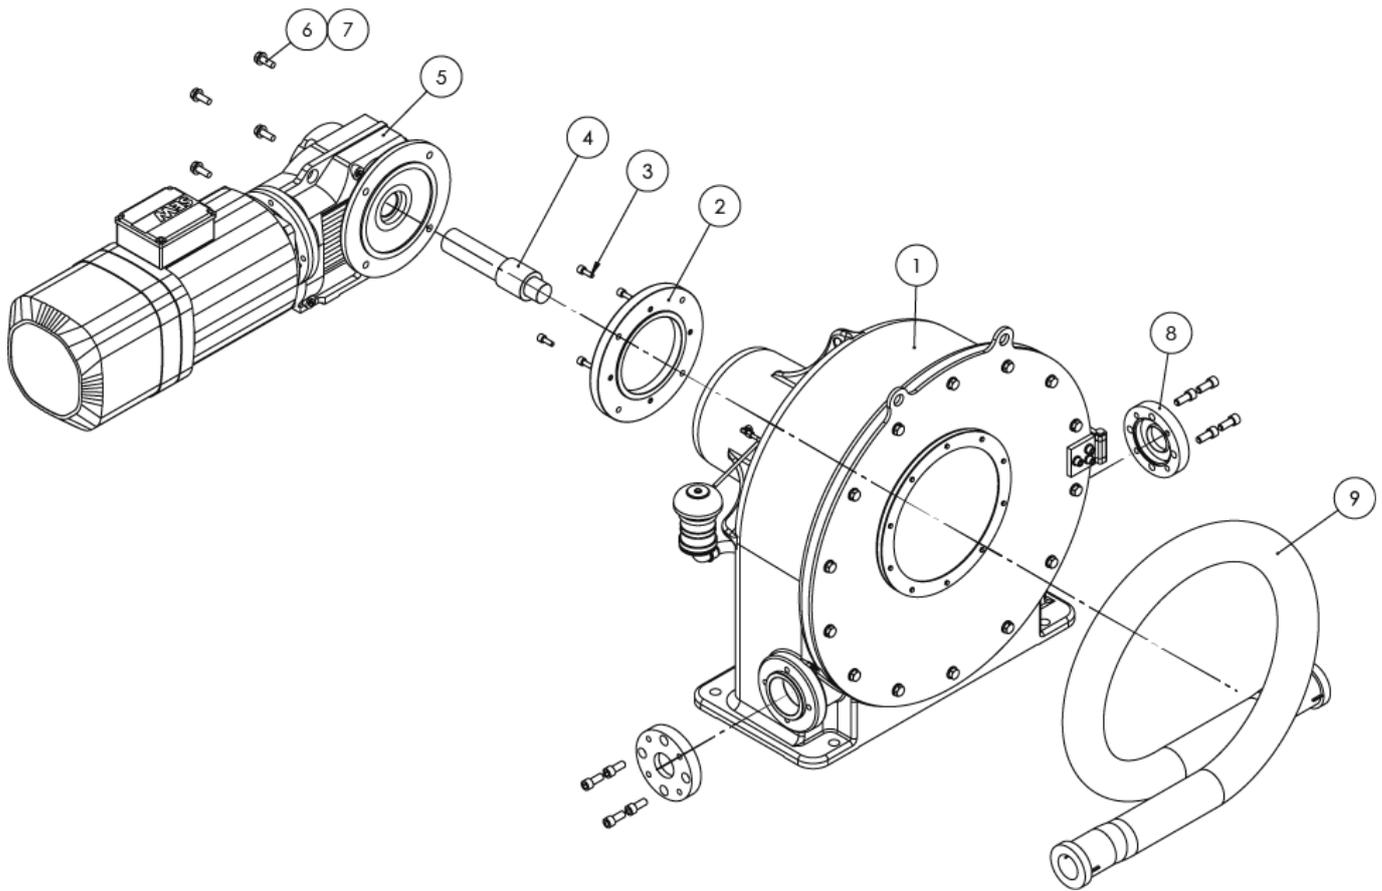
Explosionszeichnung der gesamten LPP-T-Pumpe
